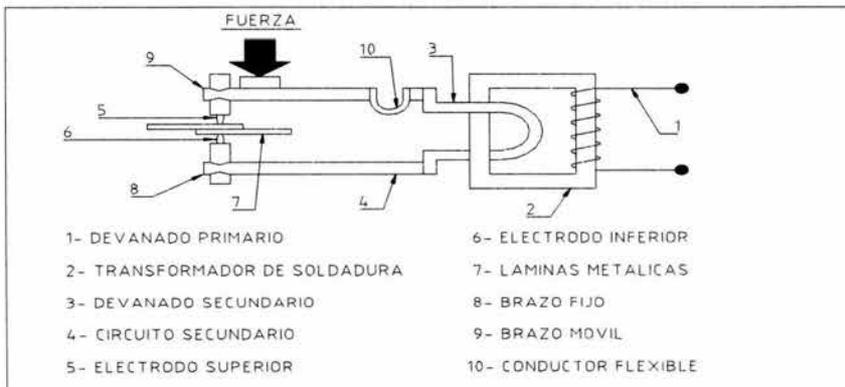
Esquema básico de una máquina para soldadura por resistencia.
